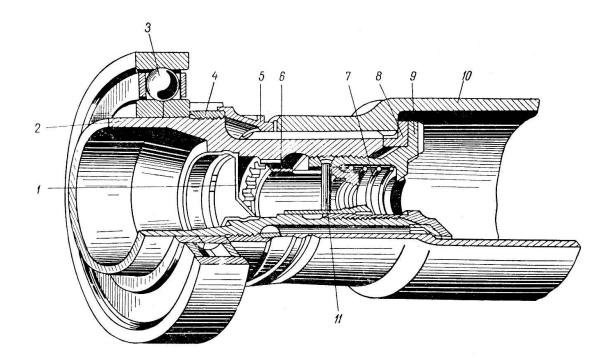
Узел соединения вала компрессора с валом турбины: 1 — заглушка; 2 — задний вал (компрессора); 3 — шарикоподшипник; 4 — гайка крепления внутренних полуколец шарикоподшипника; 5 — дистанционная втулка; 6 — шлицевая втулка; 7 — пружина; 8 — упорная втулка; 9 — болт; 10 — вал турбины; 11 — палец.
